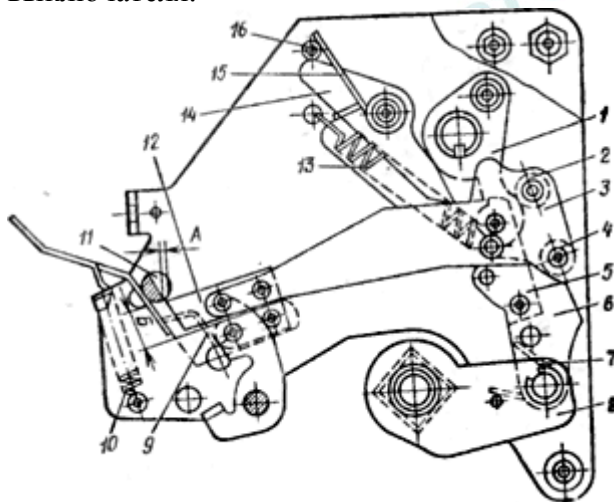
Механизм свободного расцепления автоматического выключателя:
